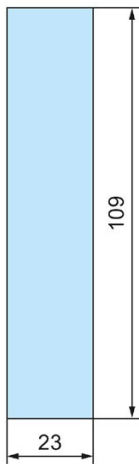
Maßbild Beschriftungstreifen für 35 mm-Module
